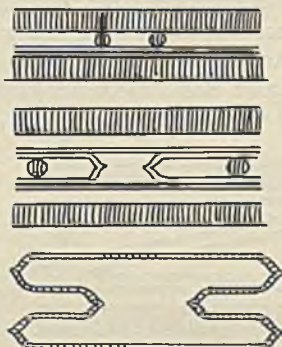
Verschweißen von 2 Blattpaaren zu einem Körper aus vier Blättern
